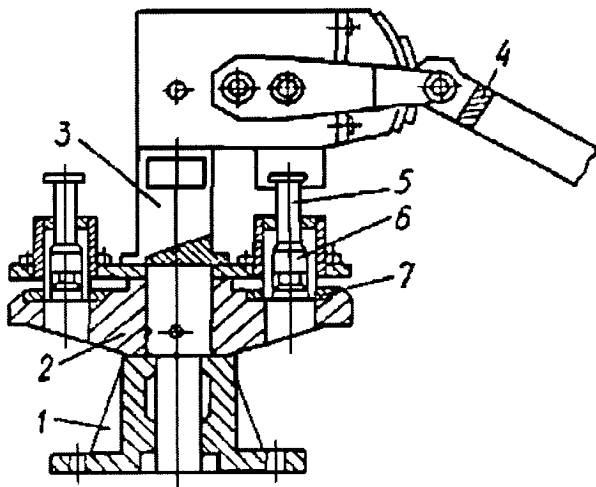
Ручний прес ПРК-8: 1 — основа; 2 — чотирипозиційна револьверна головка; 3 — корпус; 4 — рукоятка; 5 — пуансон; 6 — напрямні втулки; 7 — матриця
